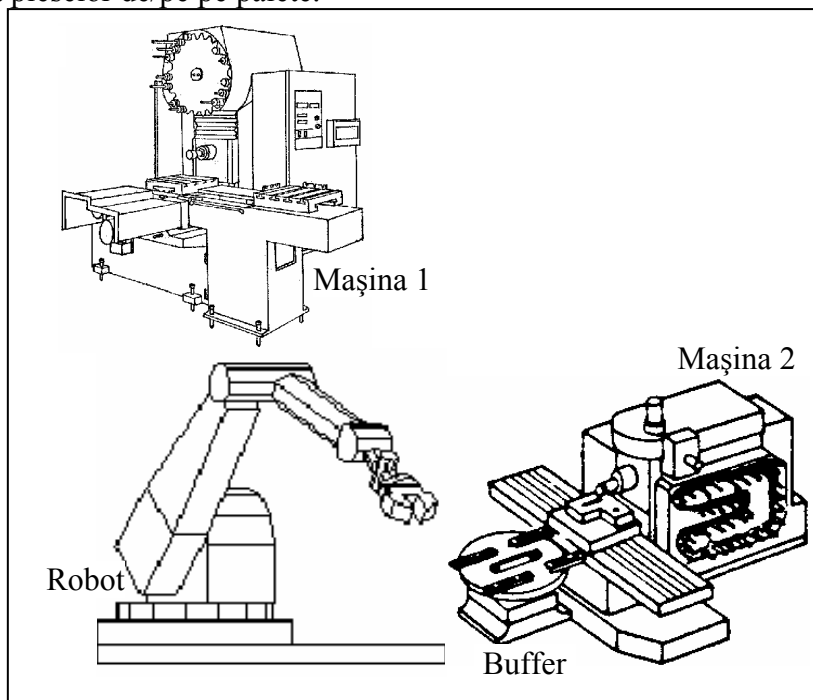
Celulă reconfigurabilă cu două centre de prelucrare, un robot de manipulare și un buffer
